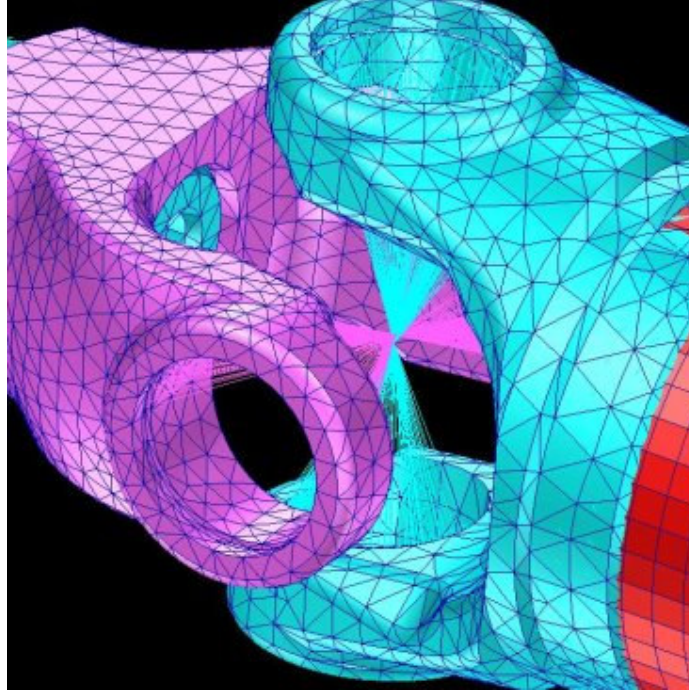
Boru- Kayıcı Mil Arasındaki Kaynak Bölgesini Temsil Eden Elemanlar
